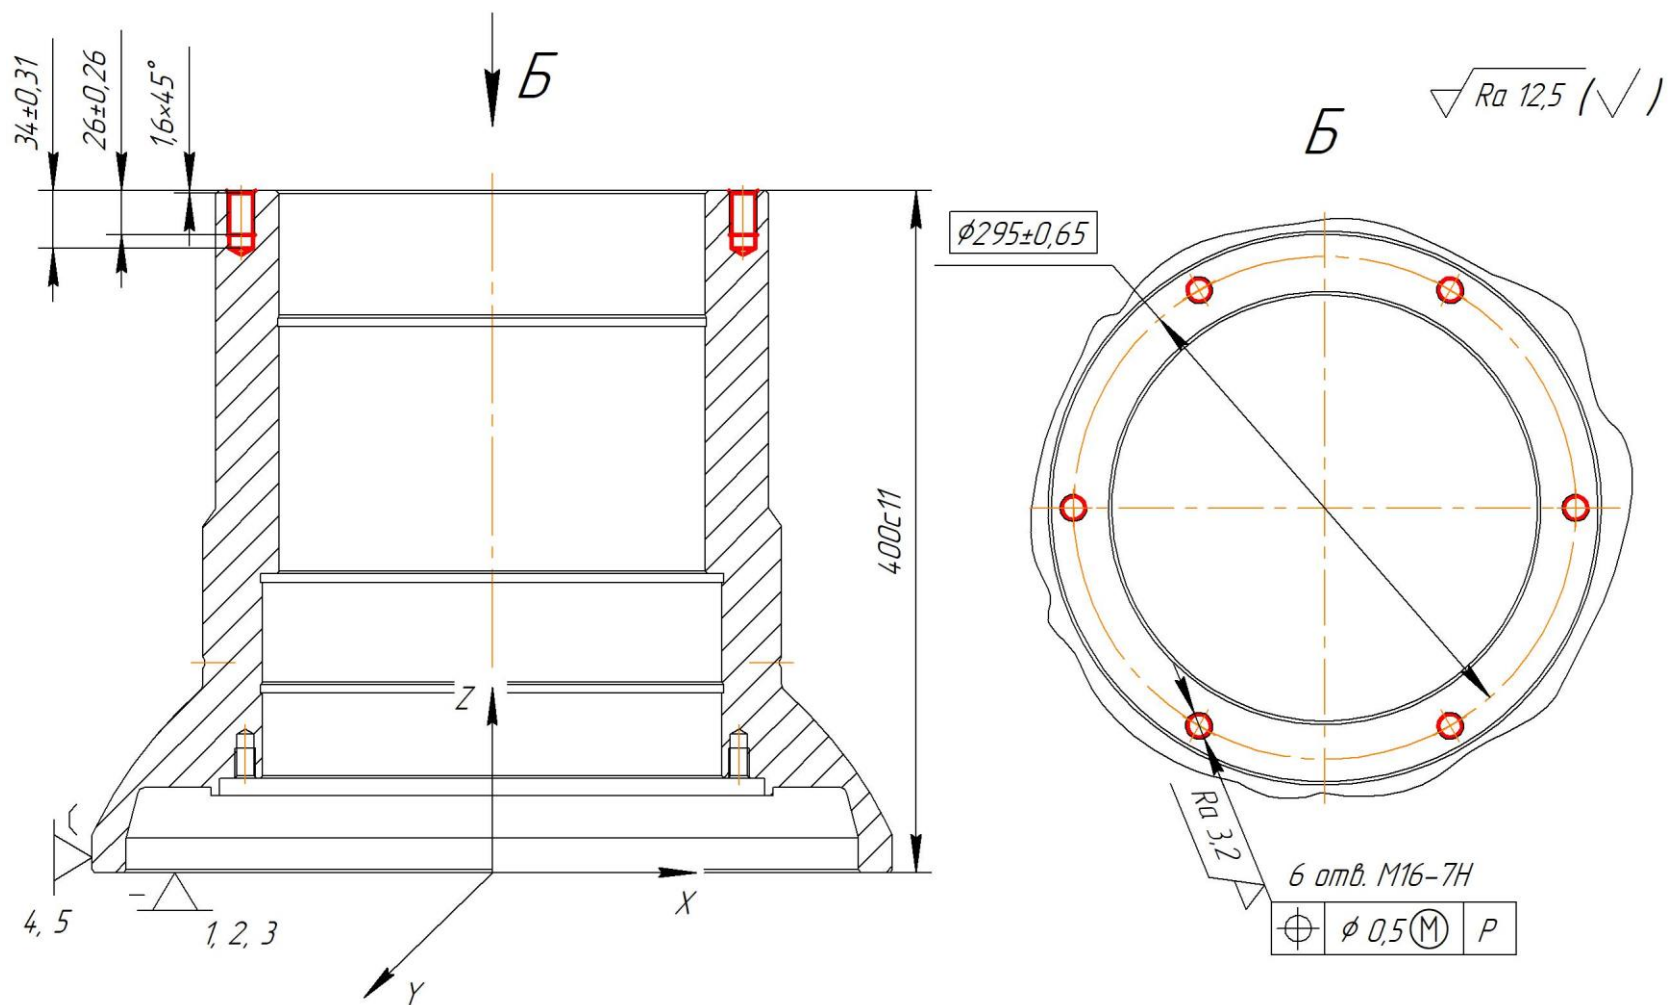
Схема базуння заготовки на операції 050 (установ Б)
